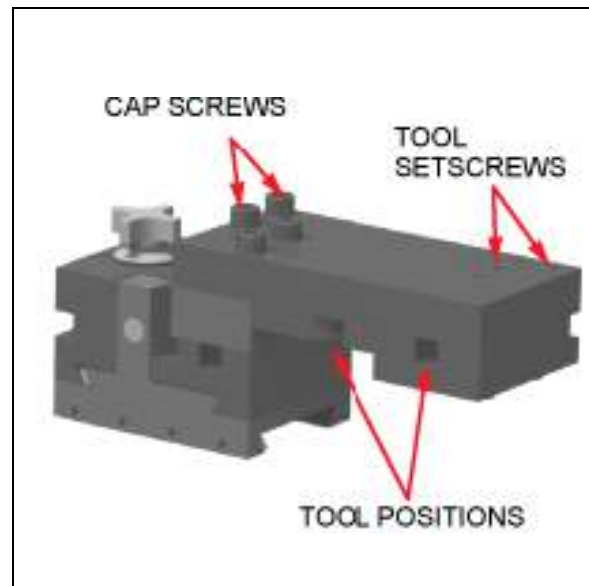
DETAIL DE L'EXTENSION DE LA TÊTE D'OUTIL
